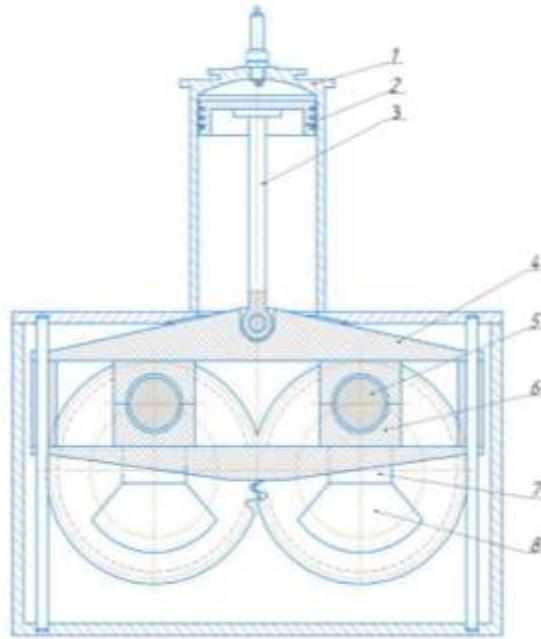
Конструктивна схема безшатунного двигуна: 1 – циліндр;
